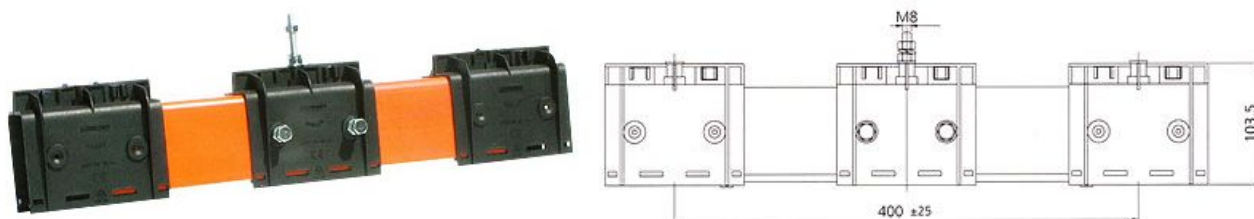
Общий вид сборочного элемента секции расширения.
